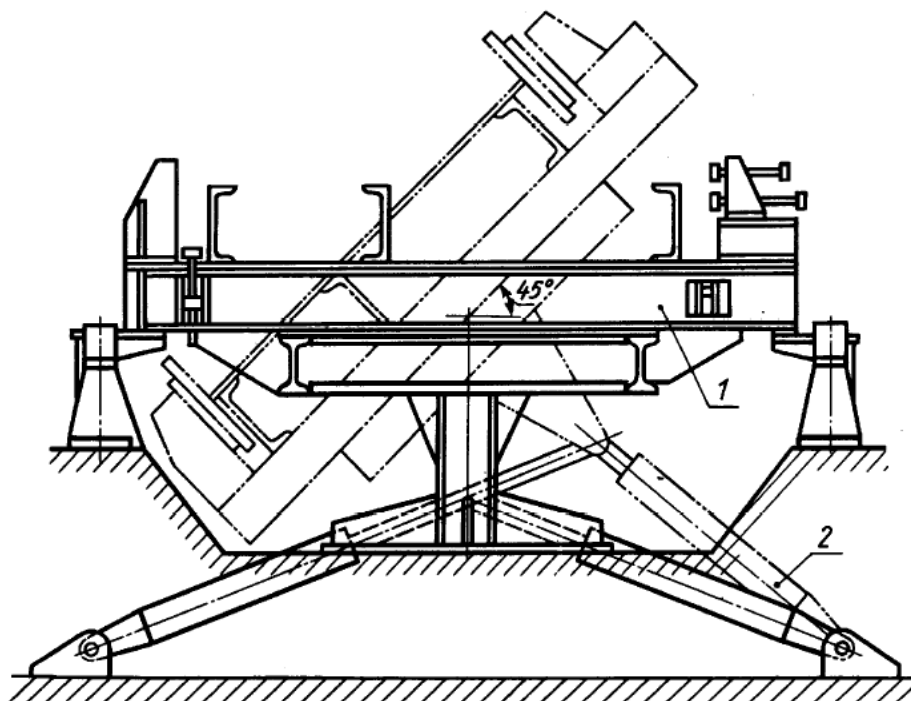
Схема полуповоротного специализированного кондуктора для сборки двутавровых балок
